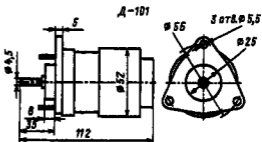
Габаритные и установочные размеры двигателей Д-101, Д-111, Д-129В, ПД3
